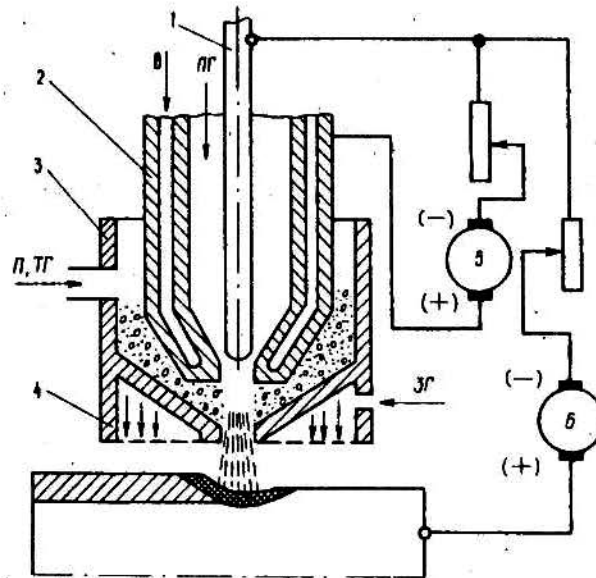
Плазмово-порошкове наплавлення: В - вода; ПГ – плазмоутворюючий газ; П - порошок; ТГ - транспортуючий газ; ЗГ - захисний газ (опис схеми даний в тексті);
